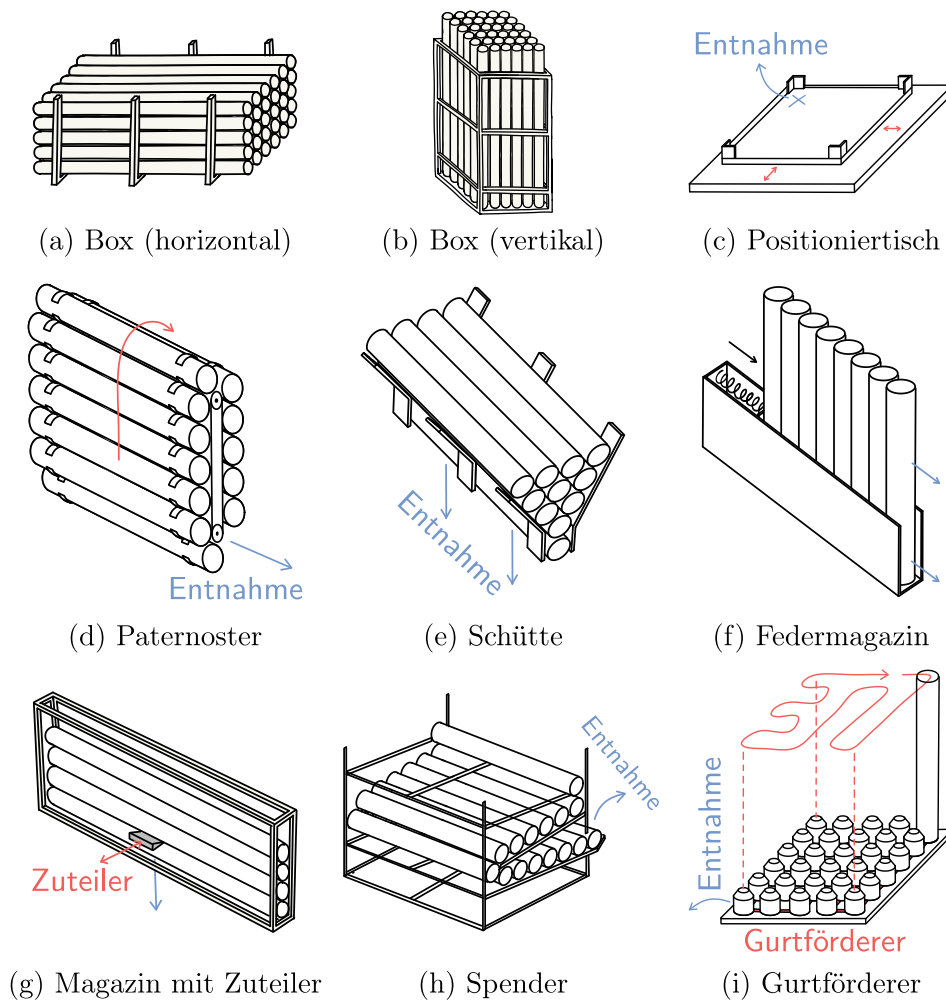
Lagerung (Speichern) der Pylonen.
